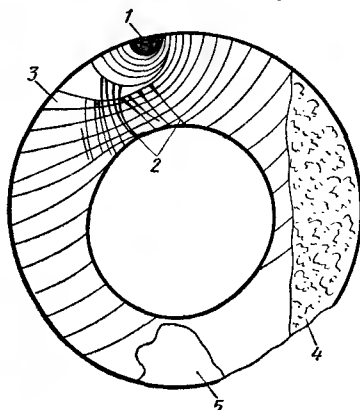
Схема усталостного излома шатунной шейки коленчатого вала:
